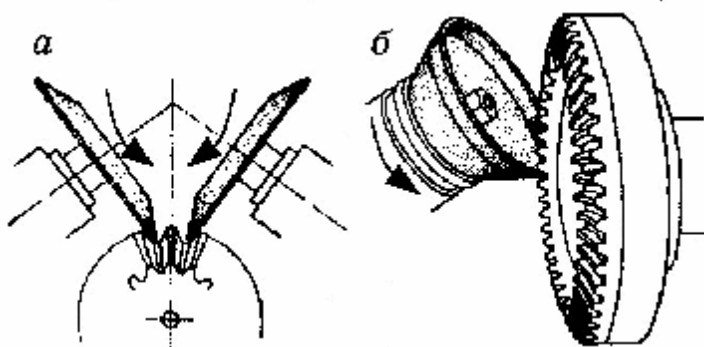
Зубошлифование конического зубчатого колеса: а — с прямым зубом; б — с криволинейным зубом
